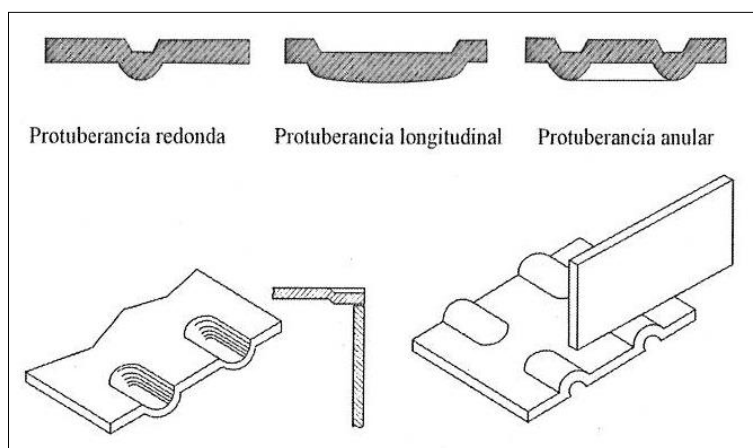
Diferentes casos de soldaduras artificiales.
